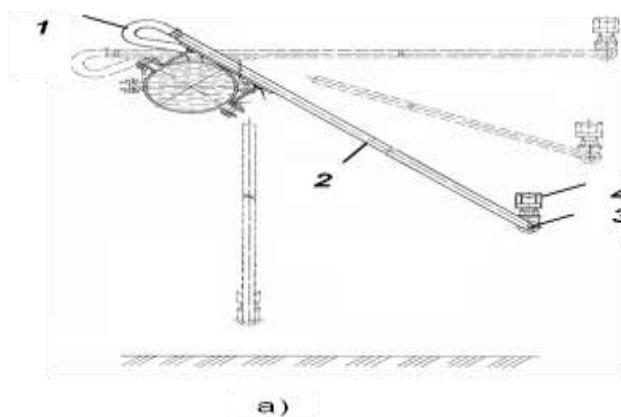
Устройство приповерхностного дождевания рычажного типа с дефлекторной насадкой
